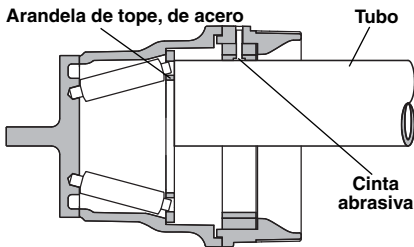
B – Posición del tubo para la limpieza externa de su extremo
